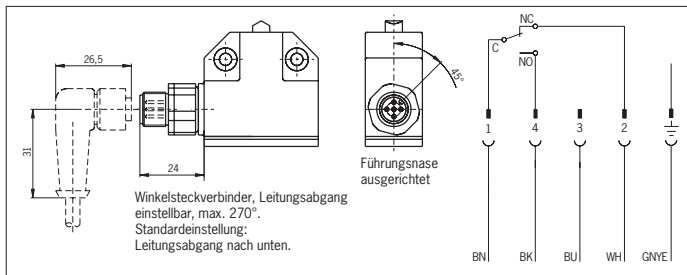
Maßzeichnung/Anschlussplan N01.550SVM5 mit Steckverbinder M12 (SVM5, 5-polig)
